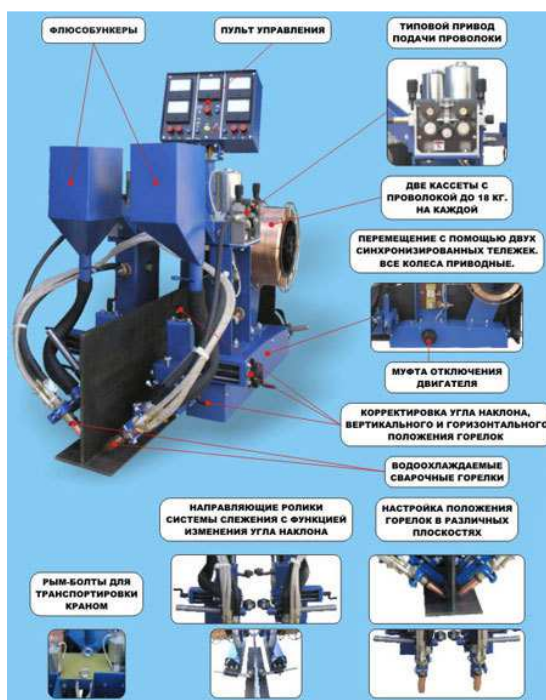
Трактор сварочный для сварки балочных конструкций
